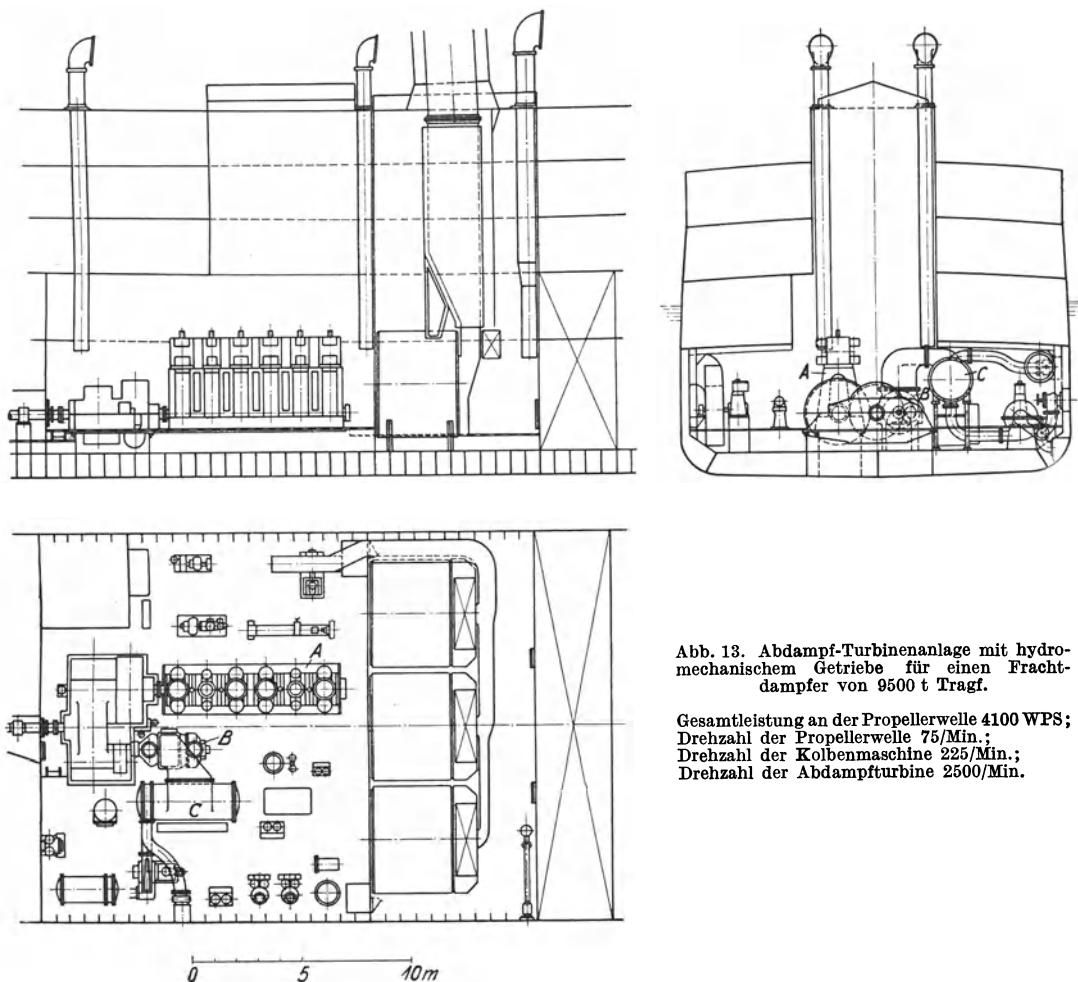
Abdampf-Turbinenanlage mit hydro-mechanischem Getriebe für einen Frachtdampfer von 9500 t Tragf.
